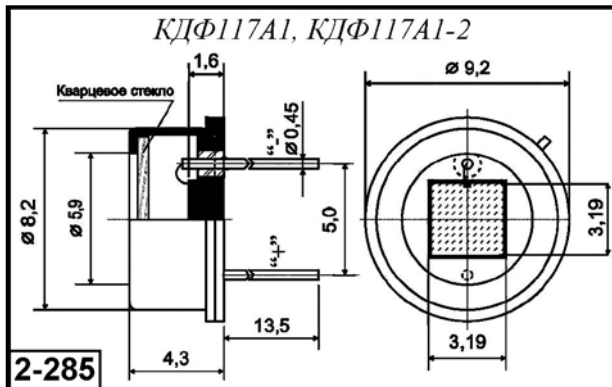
а. Внешний вид и габаритные размеры кремниевых фотодиодов
